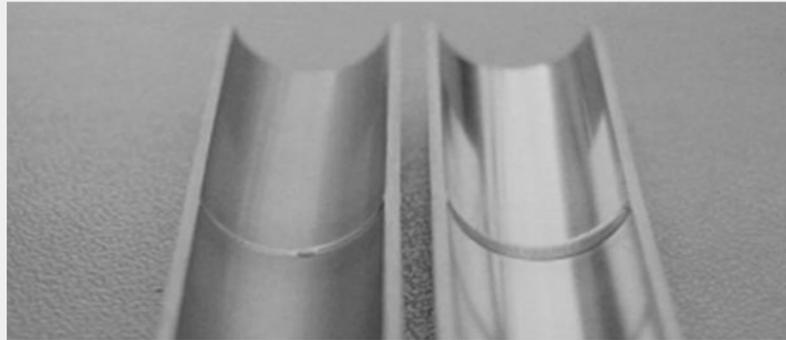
Échantillons de soudure d'un tube, en version de surface recuit brillant (BF (Bright Finished)) et nettoyé électrochimiquement (source : Dockweiler AG)
